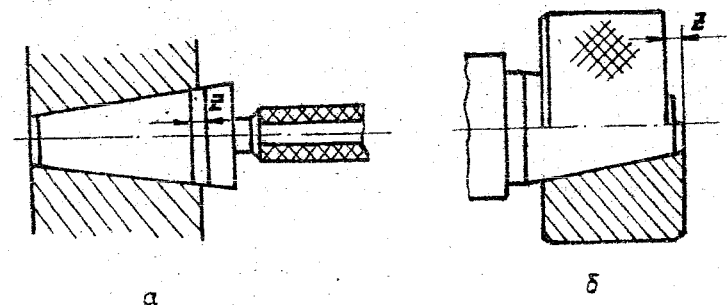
Контроль с помощью калибра-пробки /а/ и калибра-втулки /б/
